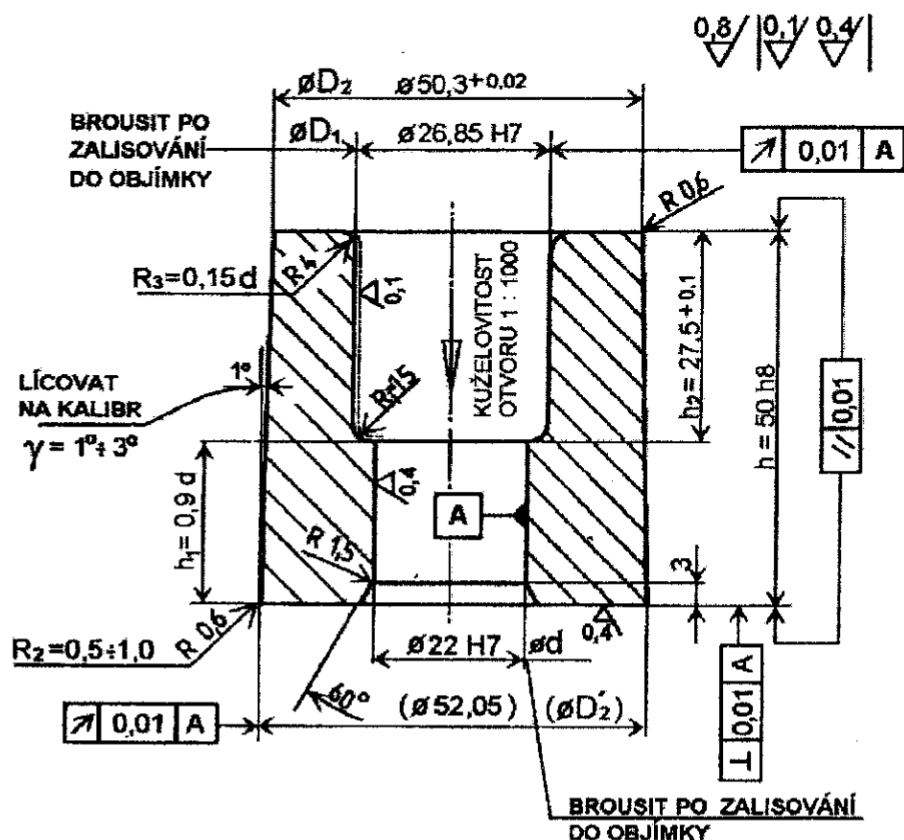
Průtlačník pro zpětné protlačování [6]
